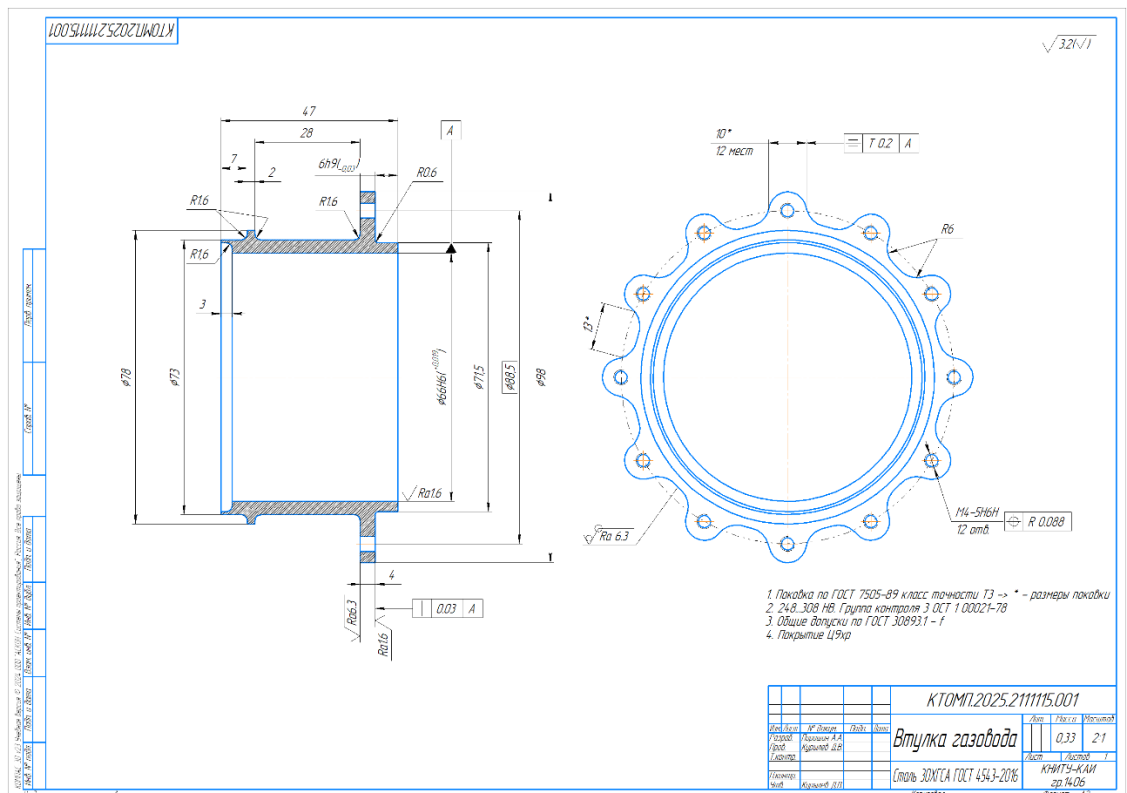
Рабочий чертеж детали «Втулка газоведа»
